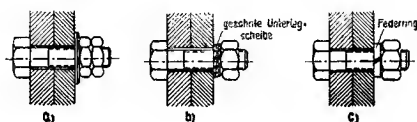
Schraubensicherung durch Gegenmutter (a), gezahnte Unterscheibe (b) oder Federring (c)
